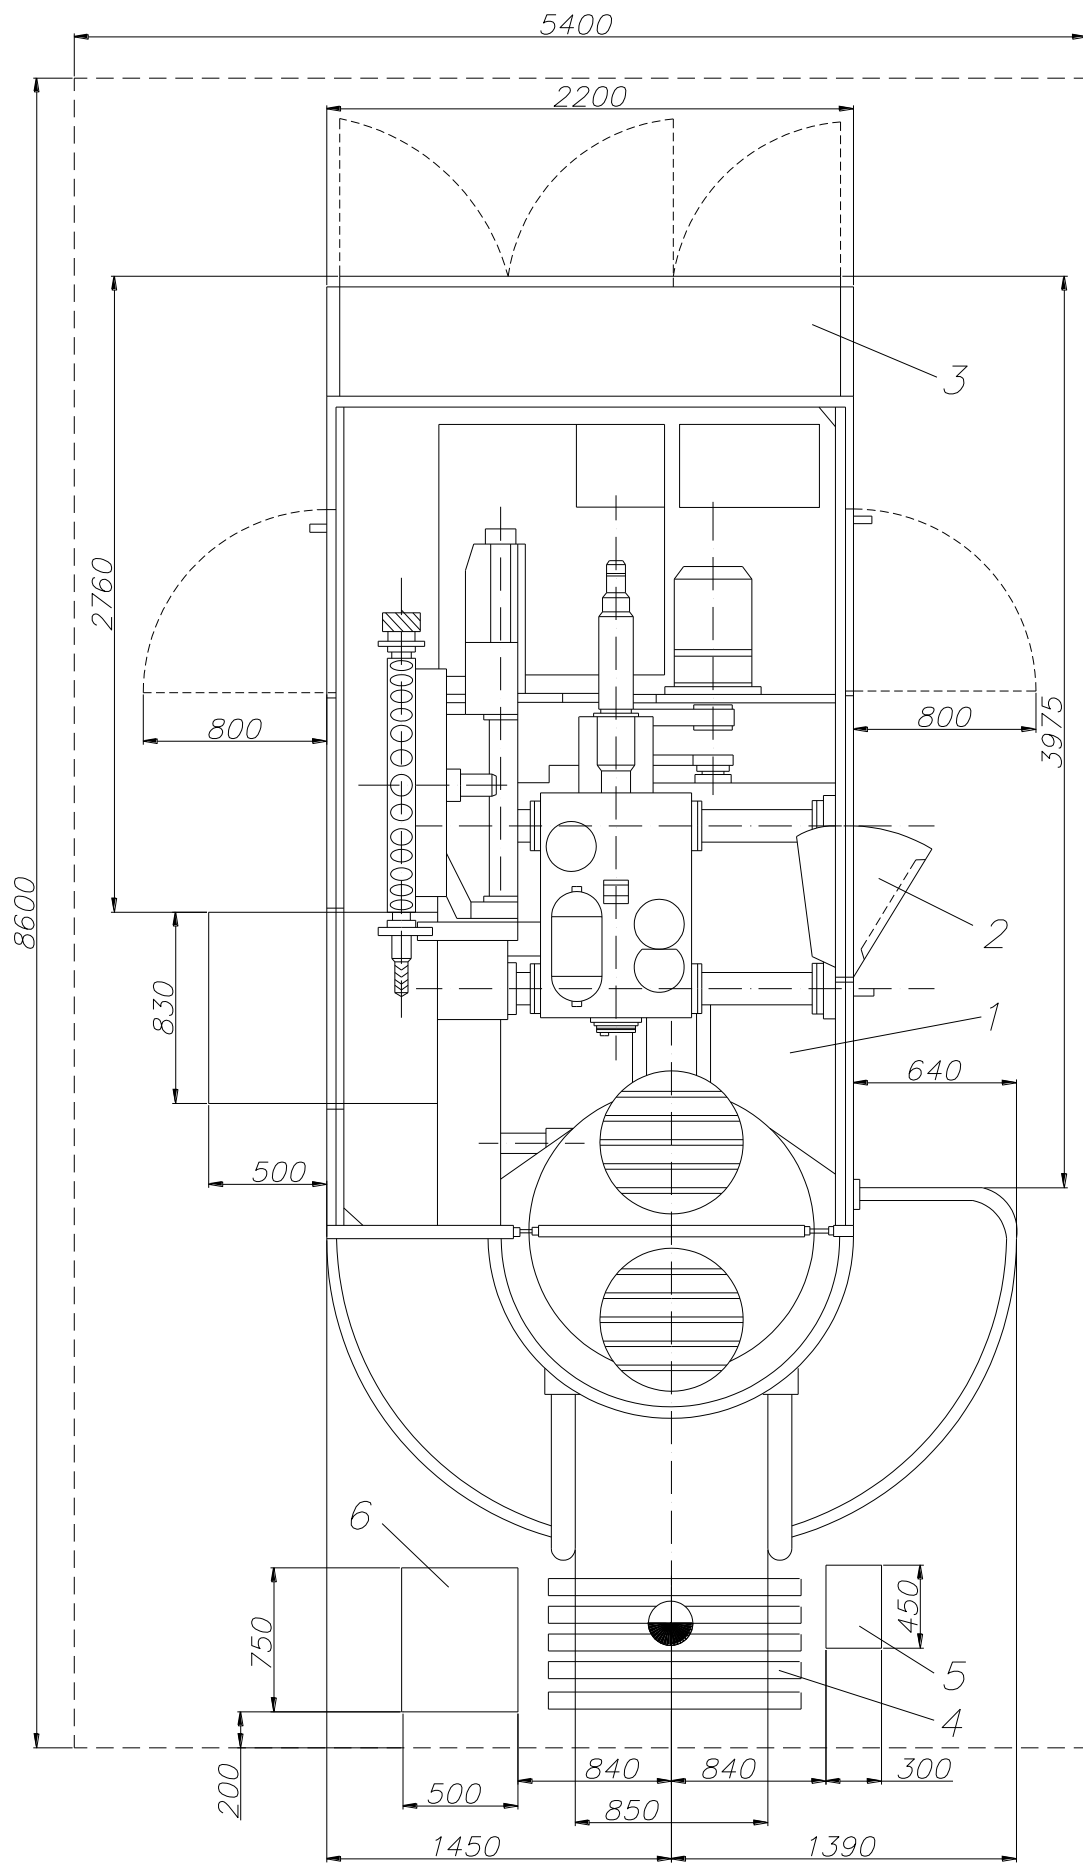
Планування робочого місця оператора проєктованого верстата: 1 – багатоцільовий верстат; 2 – система ЧПК; 3 – стелаж для заготовок та деталей
